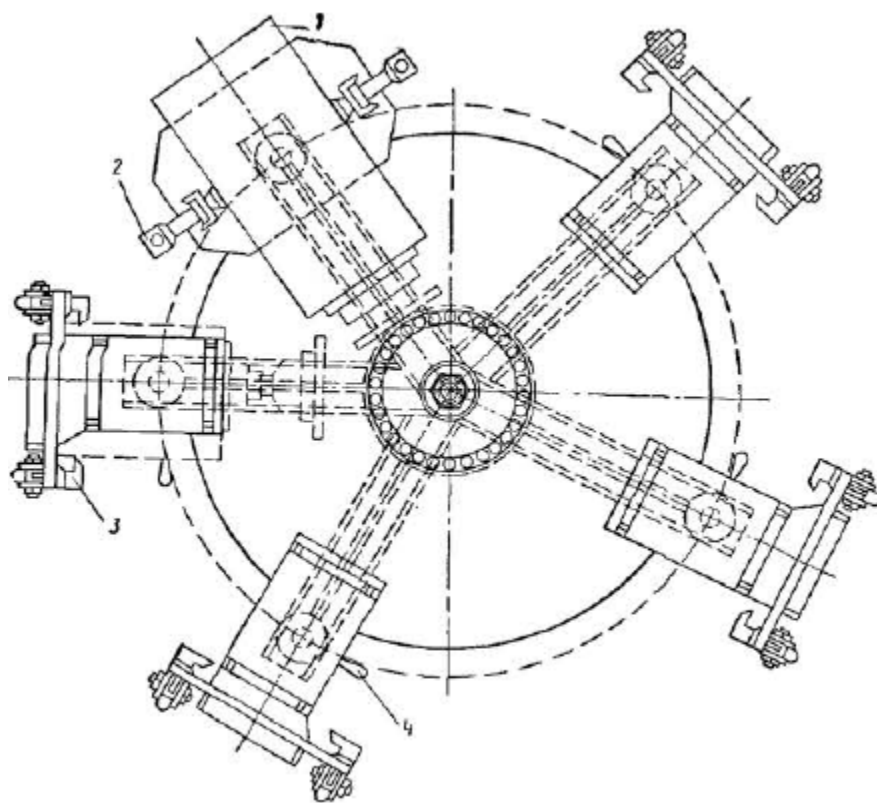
Поворотний стенд для розбирання коробок передач
